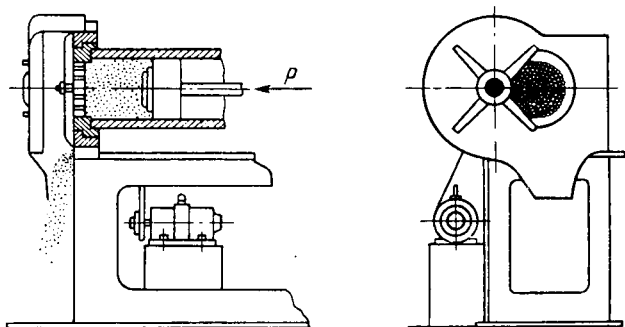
Установка для изготовления керамического флюса; рубка подаваемой массы на кусочки
